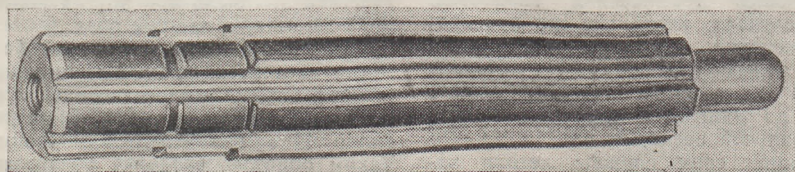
Главный вал коробки передач ГАЗ-ММ.
